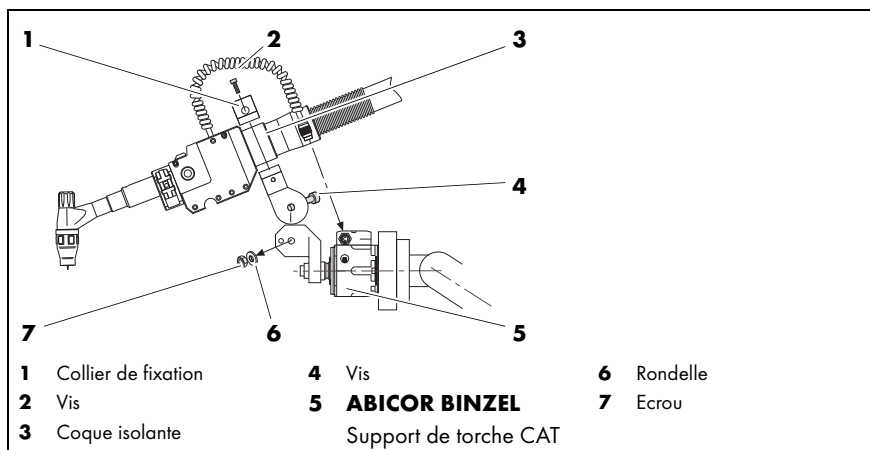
Monter le système de torche de soudage TIG sur le robot.
